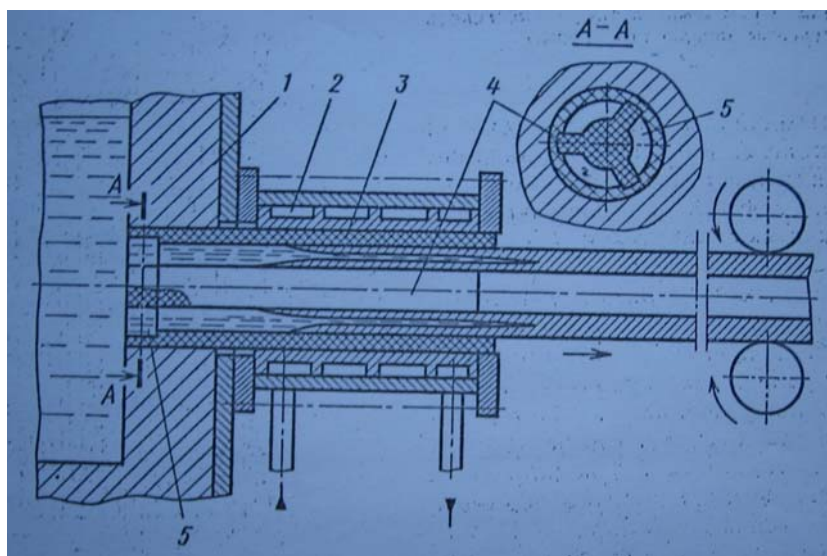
Схема кристаллизатора для горизонтального непрерывного литья трубчатых заготовок и профилей.
